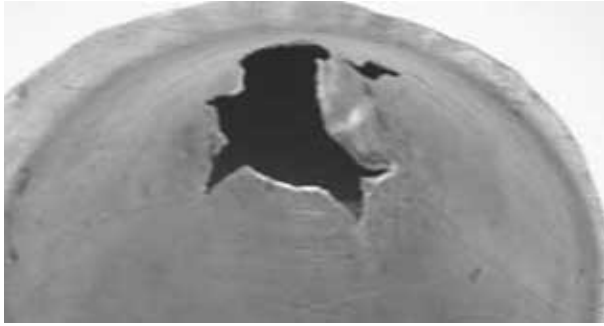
Типовой разрыв заготовки при формообразовании конической детали электрогидроимпульсным способом
